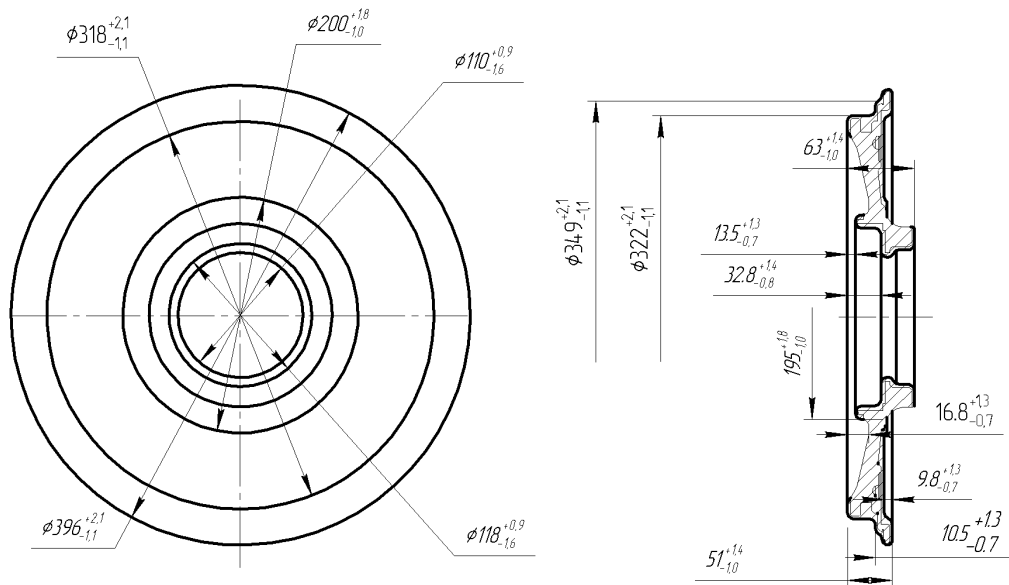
Ескіз заготовки деталі «Кришка КР33-18.350»
